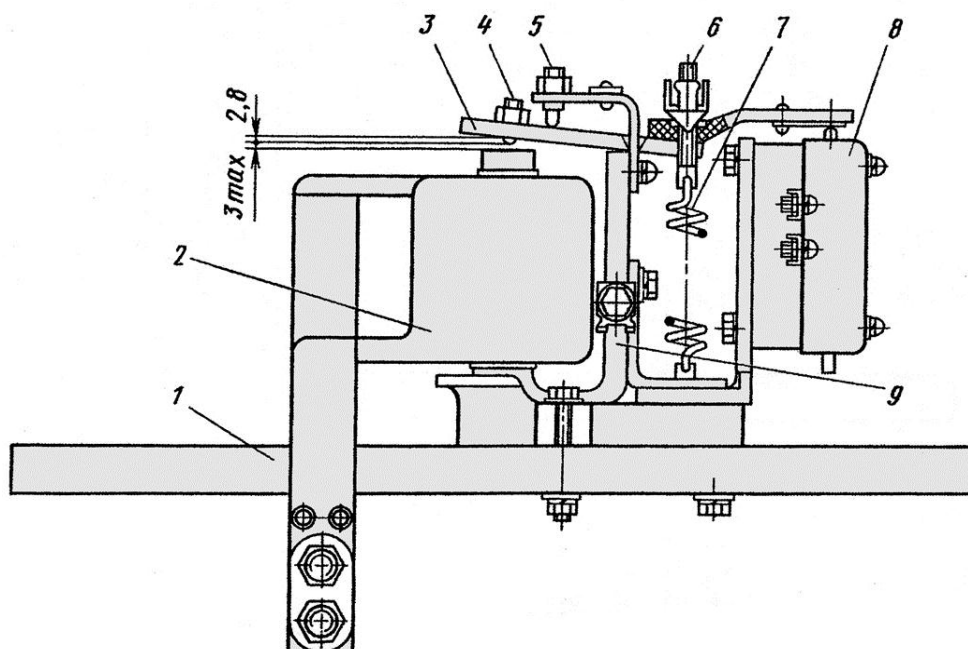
Реле тока РТ-612: 1 - панель; 2 - катушка; 3 - якорь; 4,5,6 - регулировочные шпильки; 7 - пружина; 8 - блок контактов; 9 - магнитопровод
